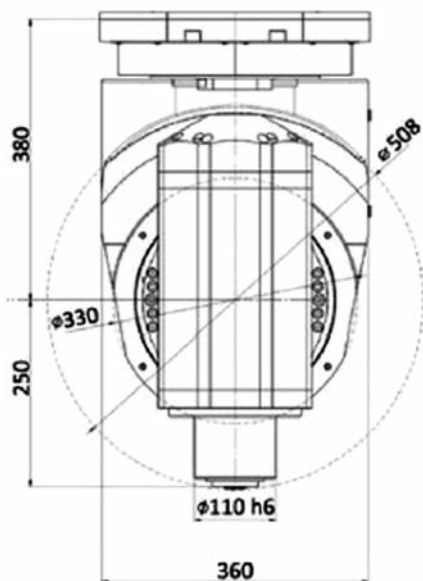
Шпиндельная головка станка HP-2616 и HPline plus
